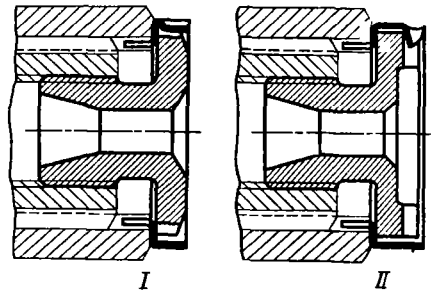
Стопорение гаек чашечной стопорной шайбой: I — гайка с наружными пазами; II — гайка с торцовыми пазами
